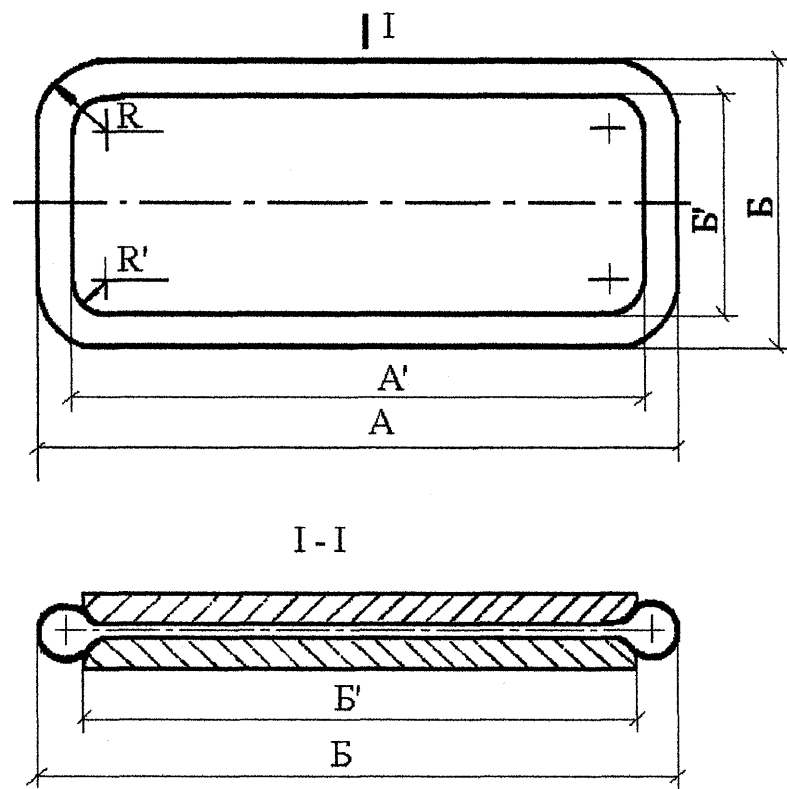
Схема к расчету плоских домкратов прямоугольного профиля
